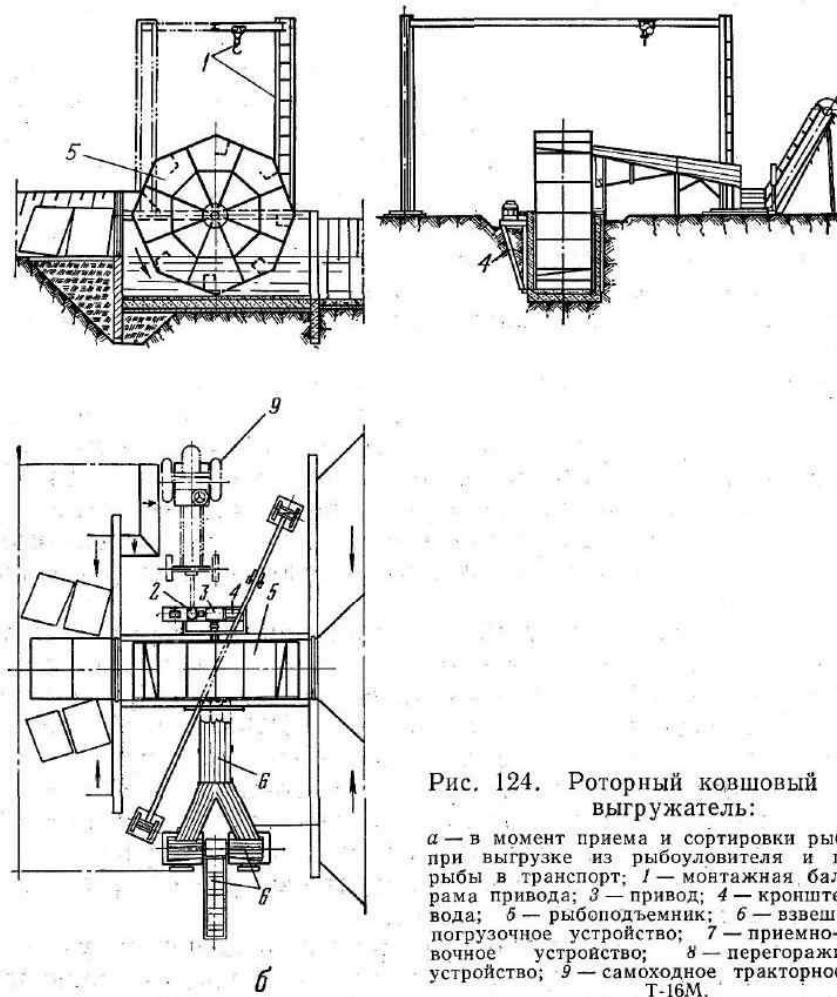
Роторный ковшовый рыбо-выгрузатель:
